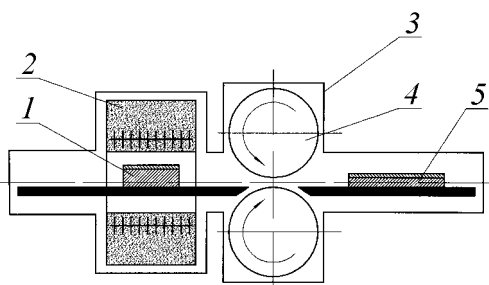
Схема вакуумной прокатки пакета: 1 – пакет до прокатки, 2 – печь, 3 – вакуумная камера, 4 – валки прокатного стана, 5 – монолитная заготовка после прокатки
